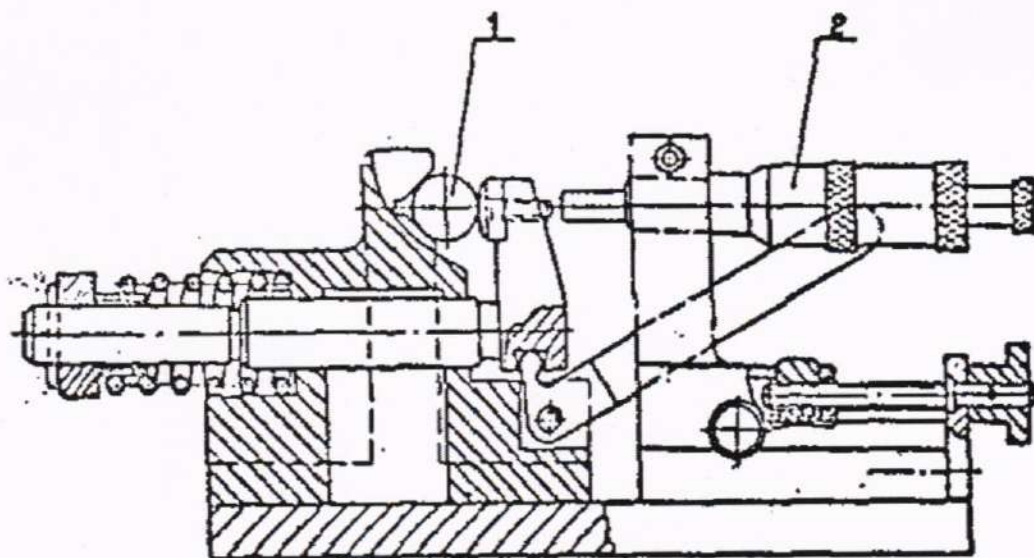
Схема приспособления с микрометрической головкой: 1 – поверяемый нутромер;
